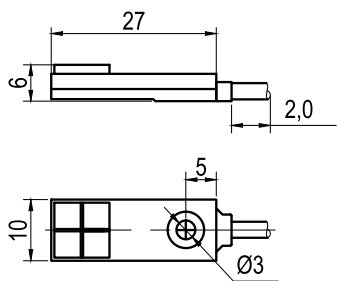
Габаритные и установочные размеры датчиков LK10
